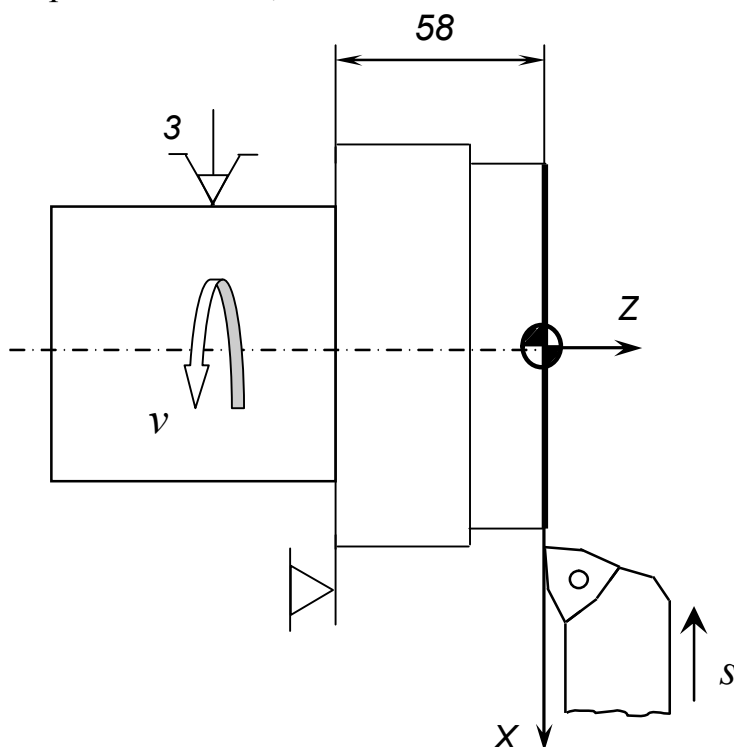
Схема виконання розмірної прив'язки прохідного-підрізного різця по осі Z
